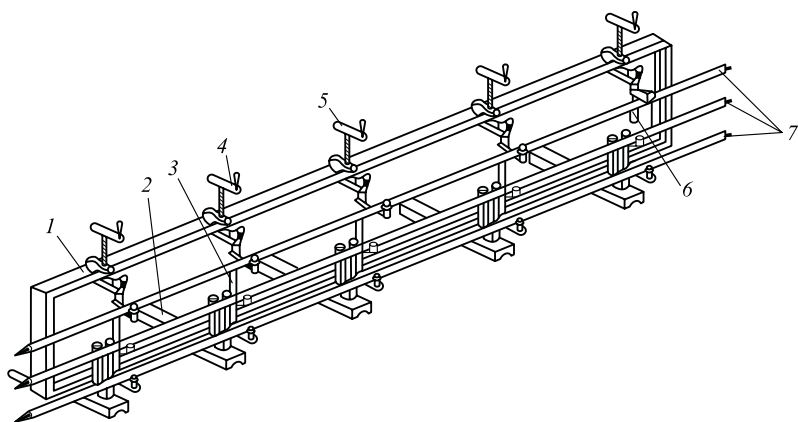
Кондуктор для сборки троллеев в блоки:
